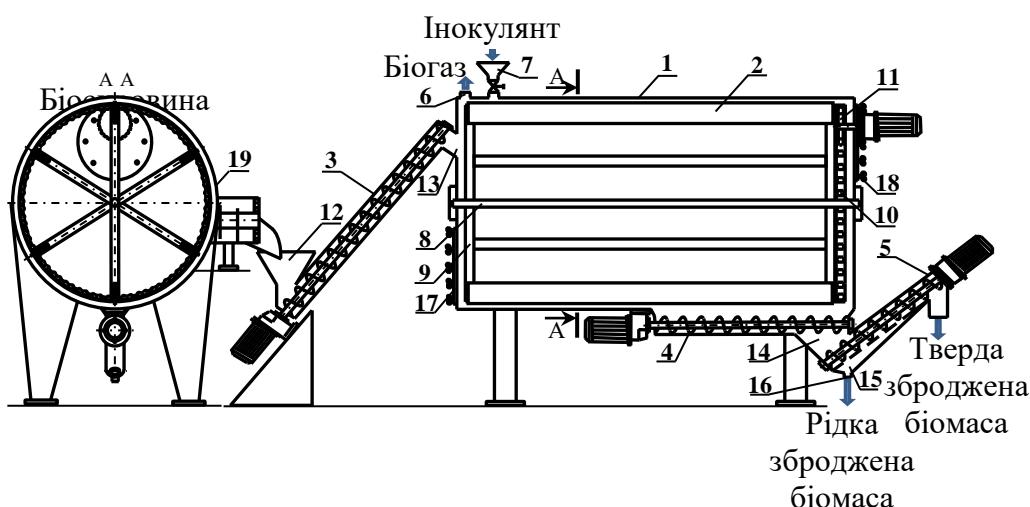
Біогазовий реактор: 1 – горизонтальний циліндричний корпус; 2 – лопатки; 3, 4, 5 – гвинтові транспортери; 6 – патрубок для відводу біогазу; 7 – пристрій для інокуляції біомаси; 8 – центральний горизонтальний вал; 9 – обертово-лопатевий механізм; 10 – кільцевий ланцюг; 11 – привідна зірочка; 12 – бункер для завантаження біомаси; 13 – патрубок; 14 – камера; 15 – камера збору рідкої збродженої фракції; 16 – патрубок для видалення рідкої біомаси; 17, 18 – люки; 19 – подрібнювач біосировини.
